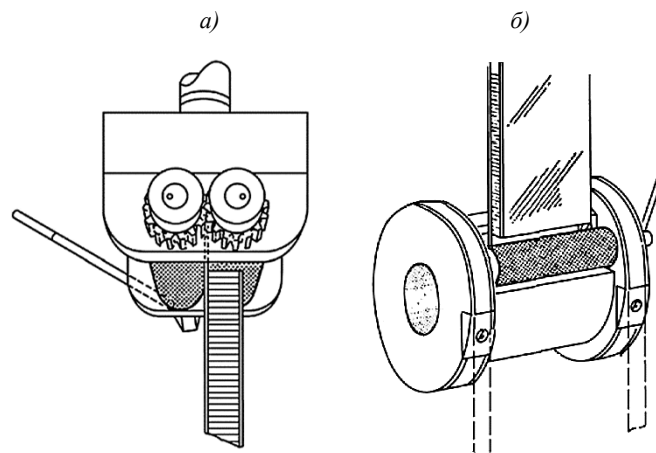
Приспособление для испытаний: *а* – зажим машины; *б* – барабан
